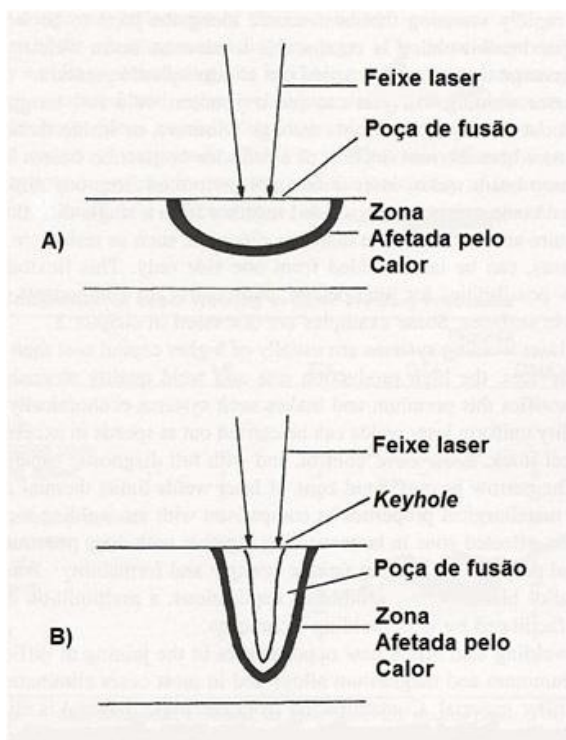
Comparação das técnicas de soldagem a laser por: (a) condução e (b) penetração<sup>71</sup>
